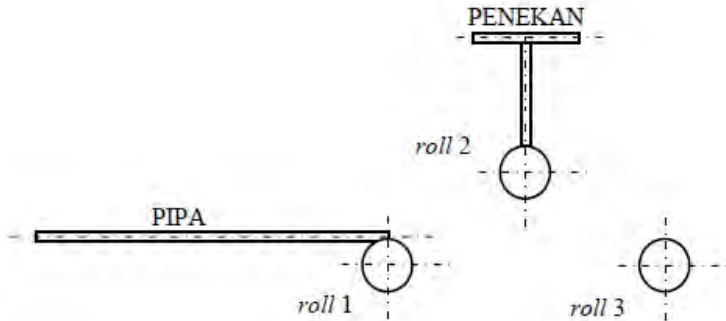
Sket mesin rol pelengkung pipa galvanis
